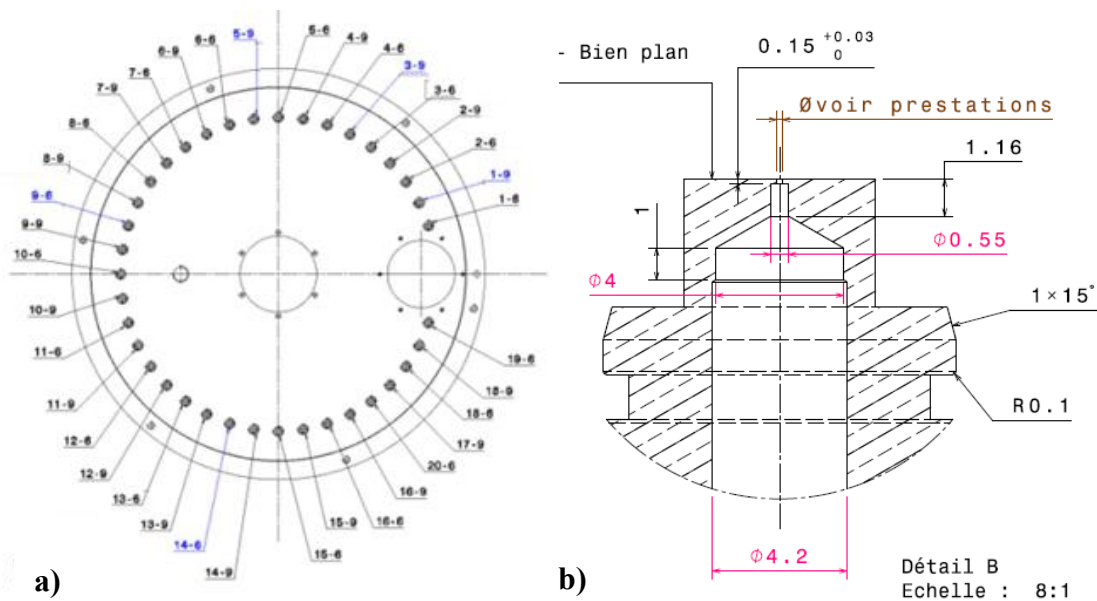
a) Plan de la couronne micropercée et b) plan de coupe d'un injecteur
